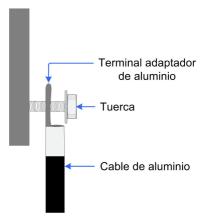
Secuencia de conexi ó n de terminal del cable de aluminio
